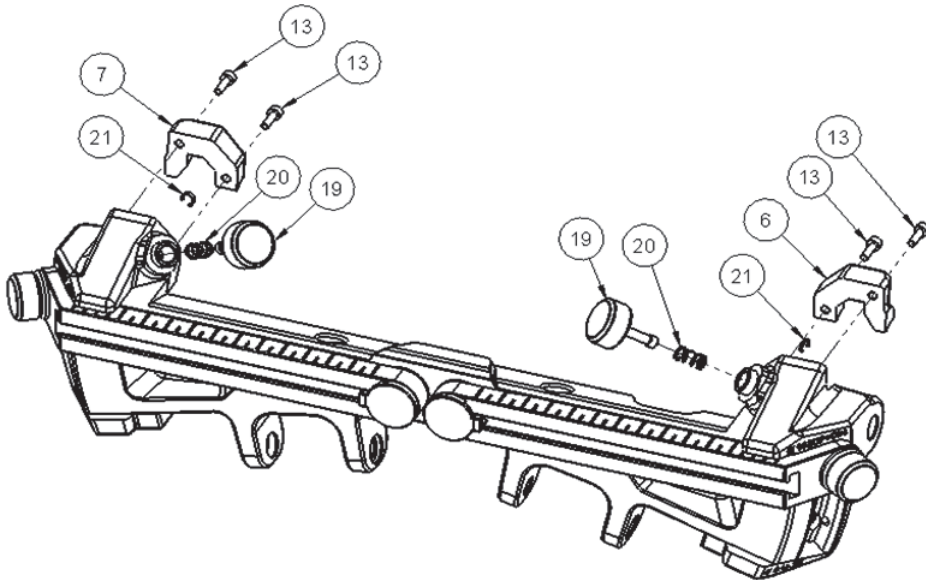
Vista detallada de montaje frontal: Parte 2
